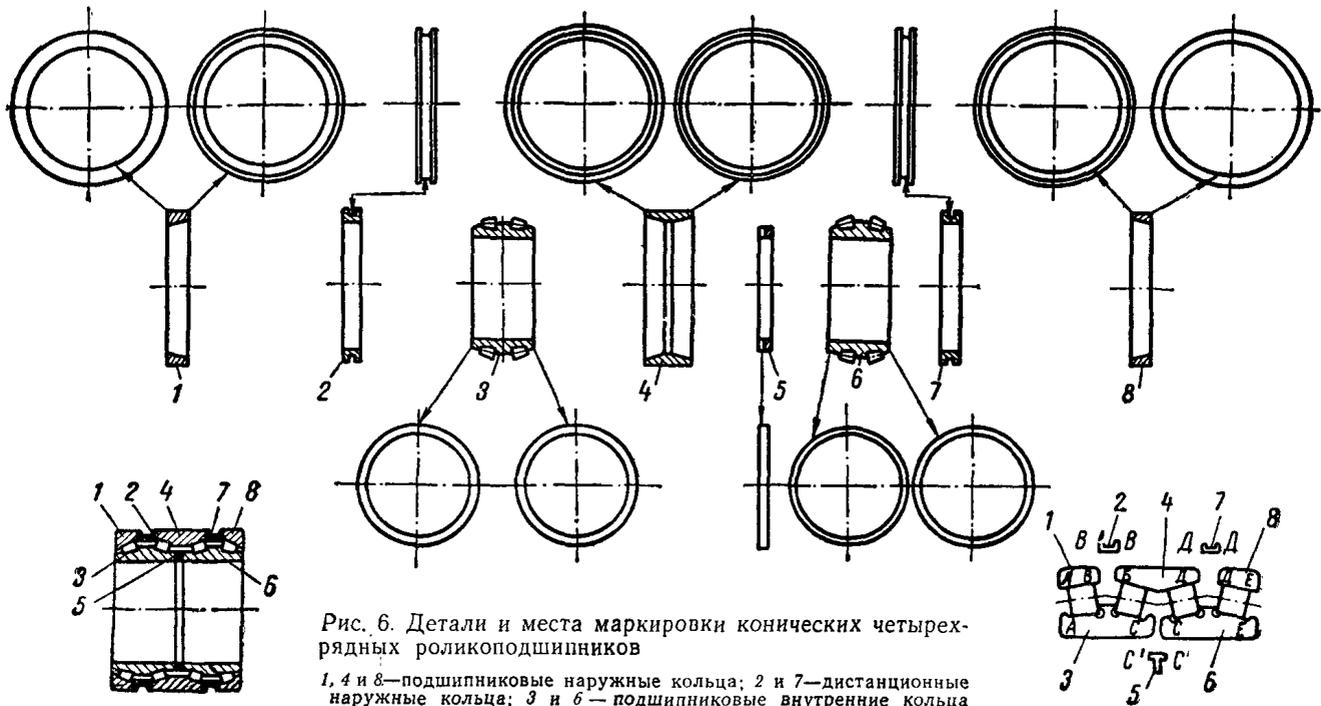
Детали и места маркировки конических четырехрядных роликоподшипников
